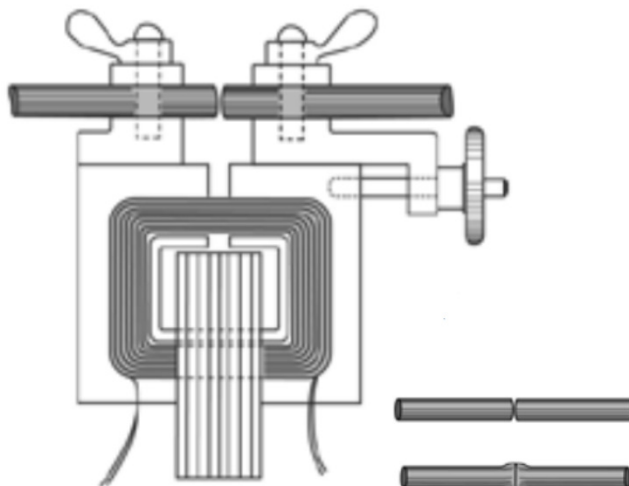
Transformador de soldagem por resistência criado por Thomson
